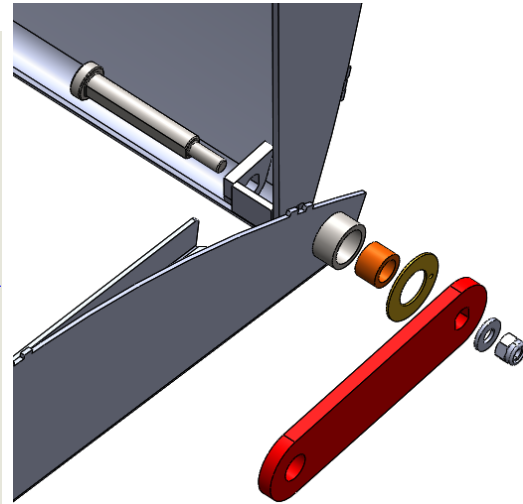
Vista explodida da montagem do eixo de transmissão.
